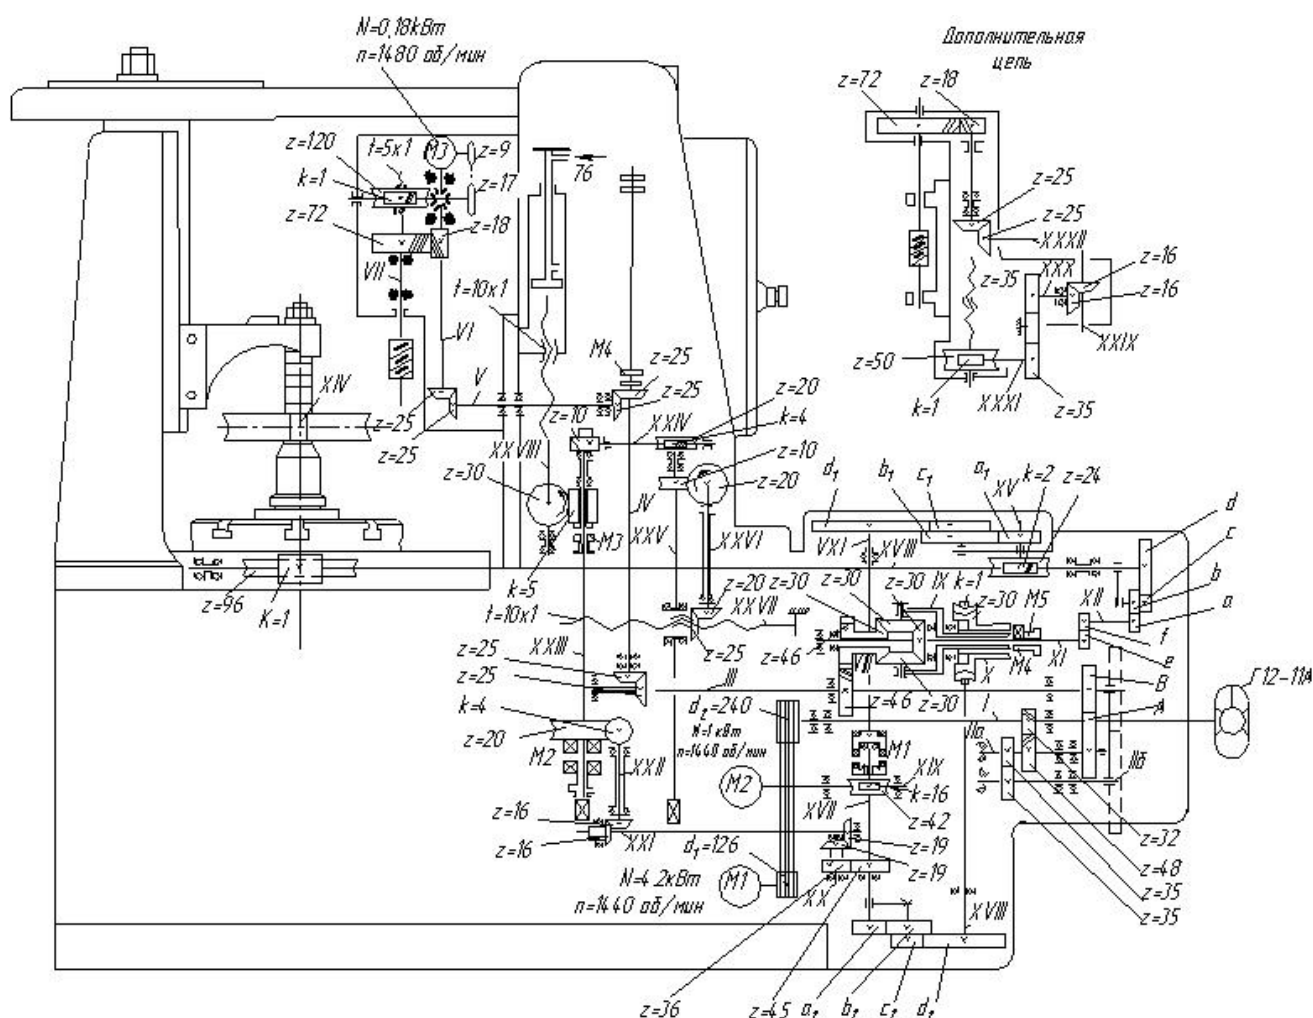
Кинематическая схема зубофрезерного станка модели 5E32
